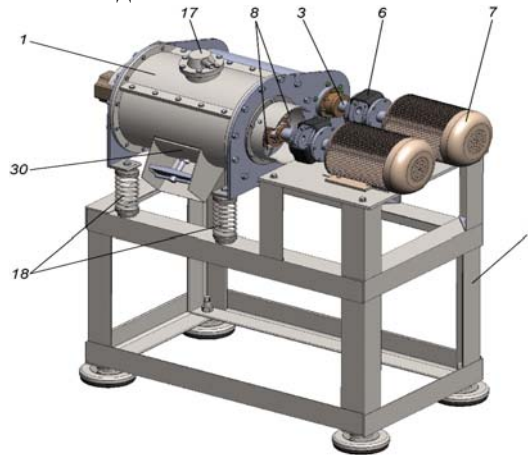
Загальний вигляд запропонованого пристрою для віброабразивної обробки деталей у автоматичному режимі (вигляд із сторони керованого дебалансного вібробуджувача)
